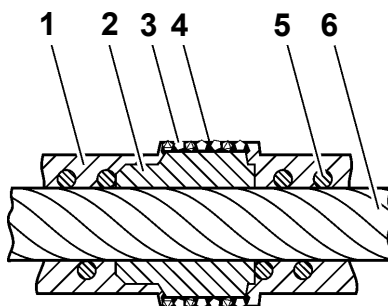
Gesinterde diamantkabel Ø 11 mm
